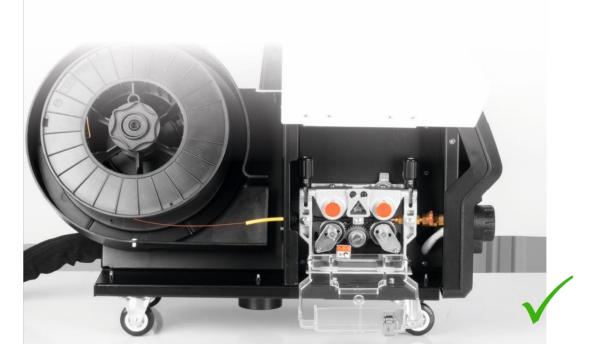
Заправка сварочной проволоки в подающий механизм
